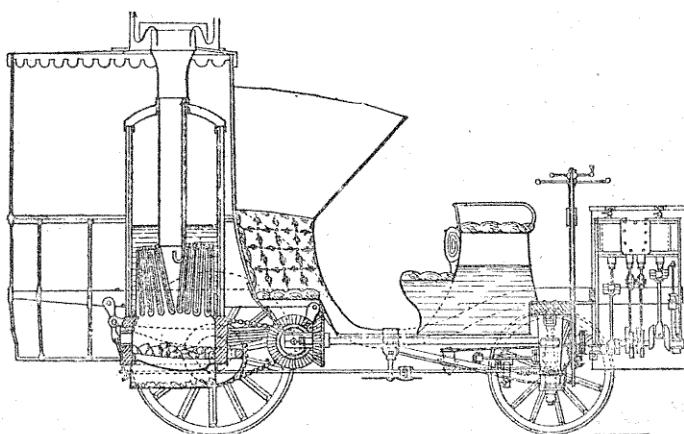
Première automobile à vapeur de Bollée (Coupe).
